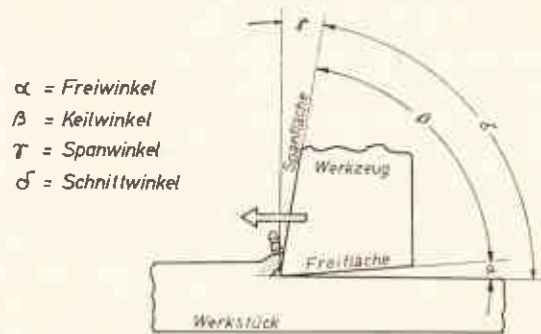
Grundform und Winkel der Werkzeugschneide
